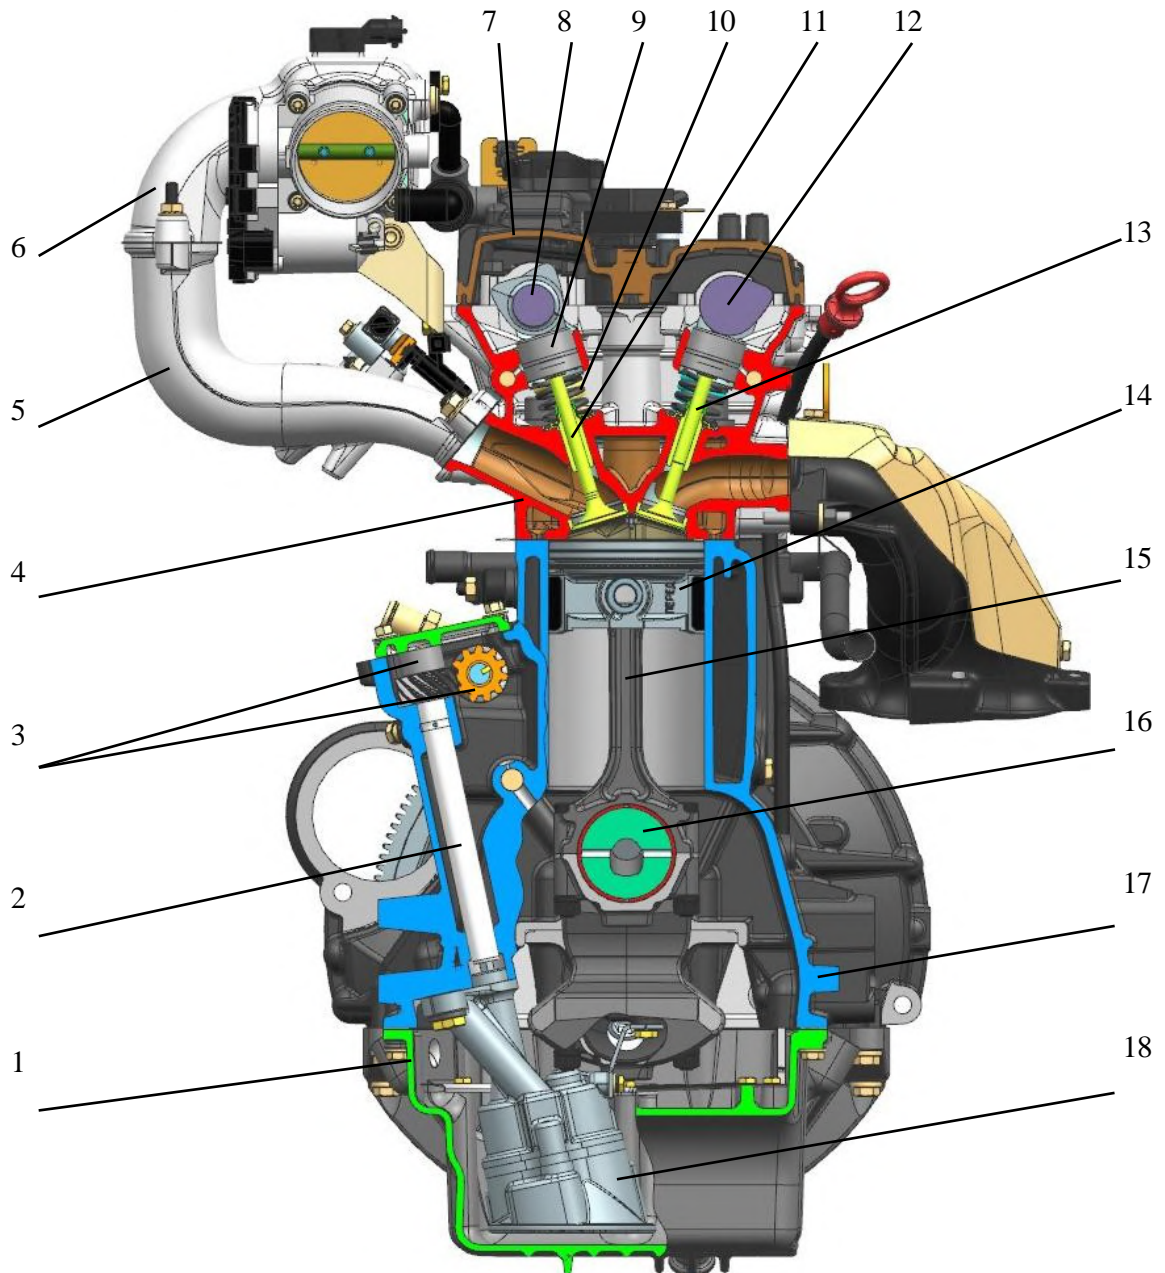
Querschnitt des Motors ZMZ-40905.10:
